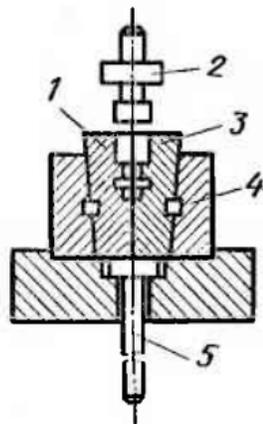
Схема штампа для штамповки в разъемных матрицах
